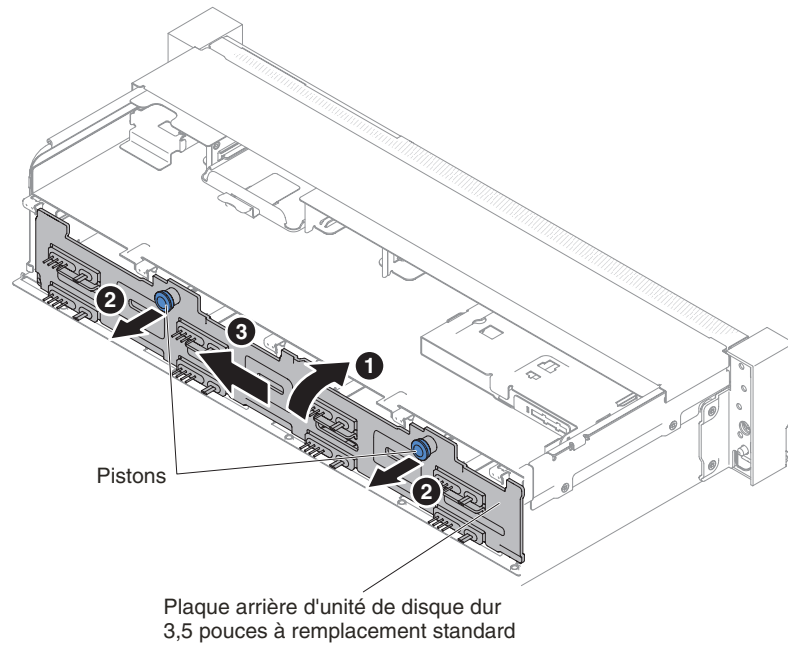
Plaque arrière à remplacement standard 3,5 pouces /fond de panier d'unité de disque dur remplaçable à chaud 3,5 pouces
